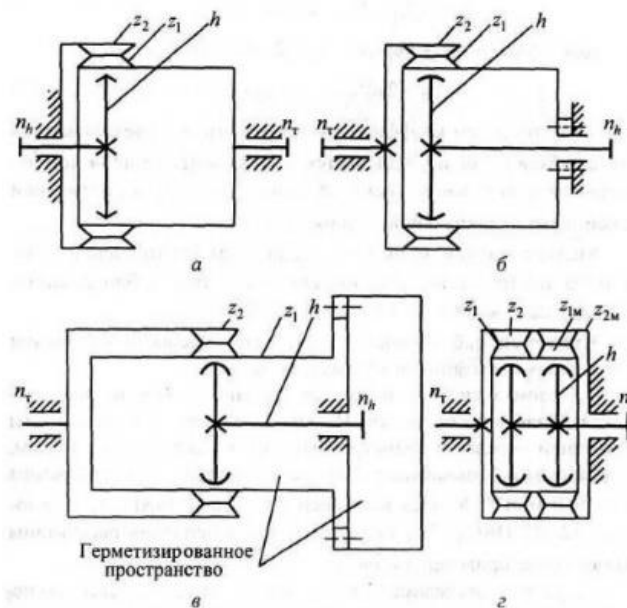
Кинематические схемы волновых зубчатых передач
